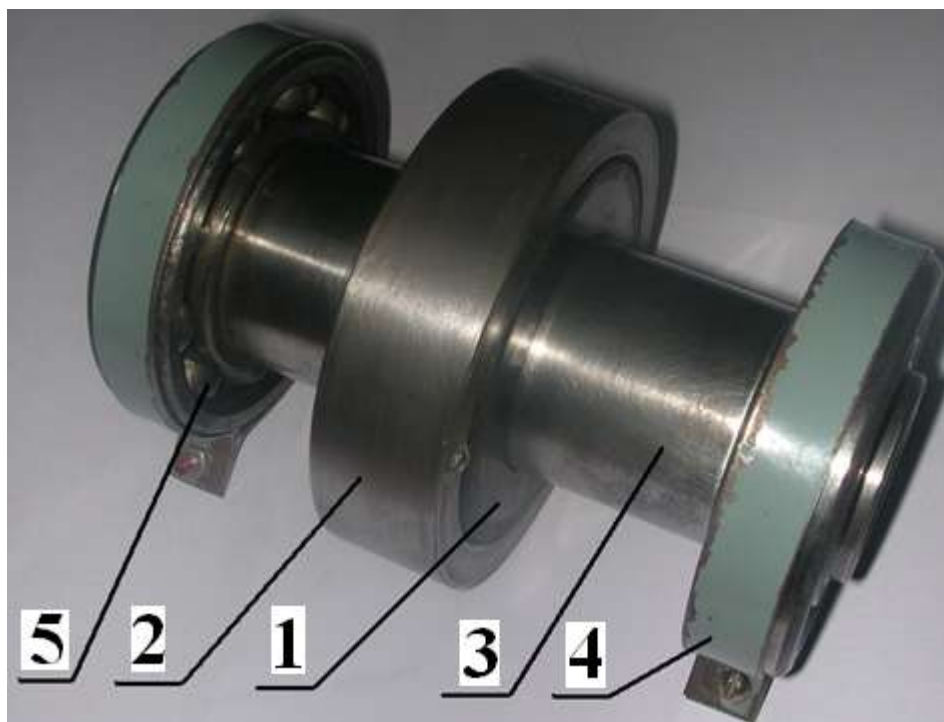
Конструкция опытного образца пьезопреобразователя
